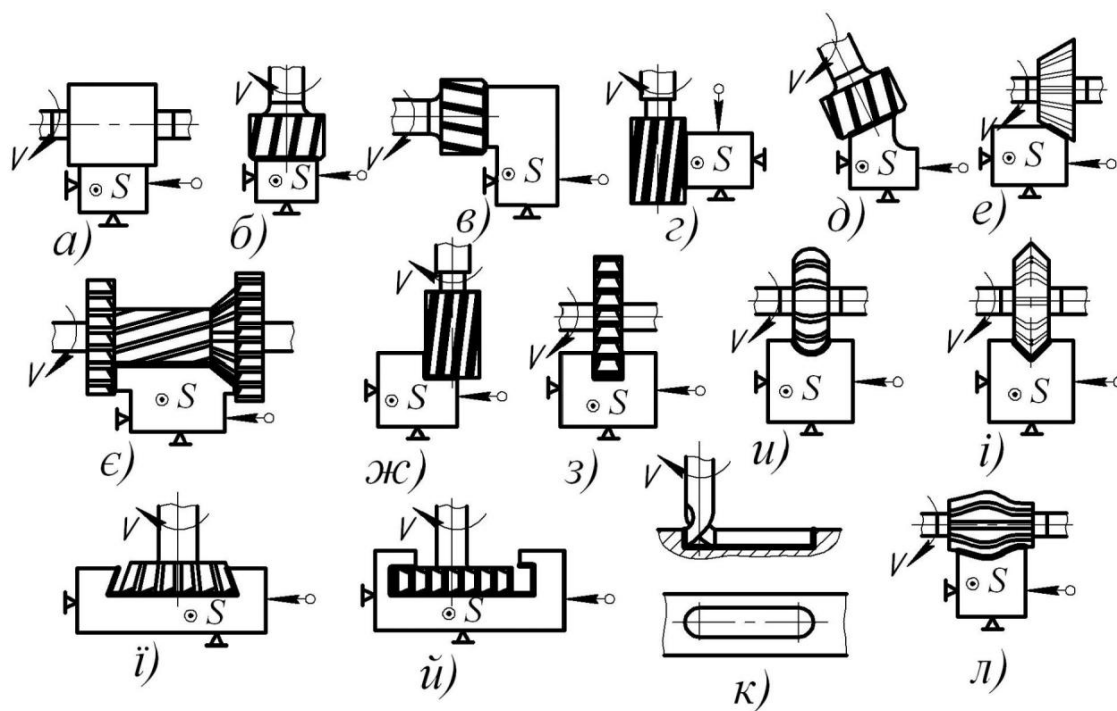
Схеми обробки заготовок на горизонтально- і вертикально-фрезерних верстатах
